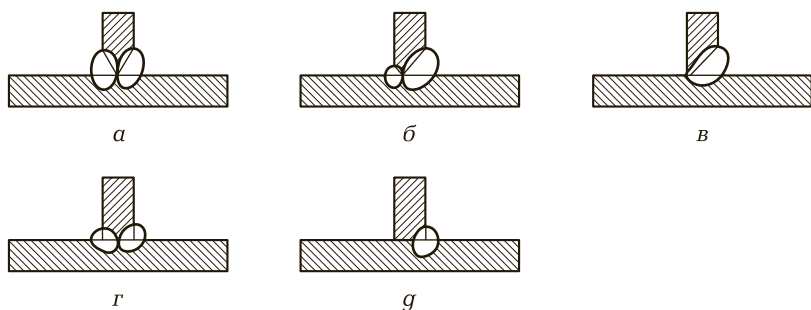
Типы тавровых сварных соединений:
